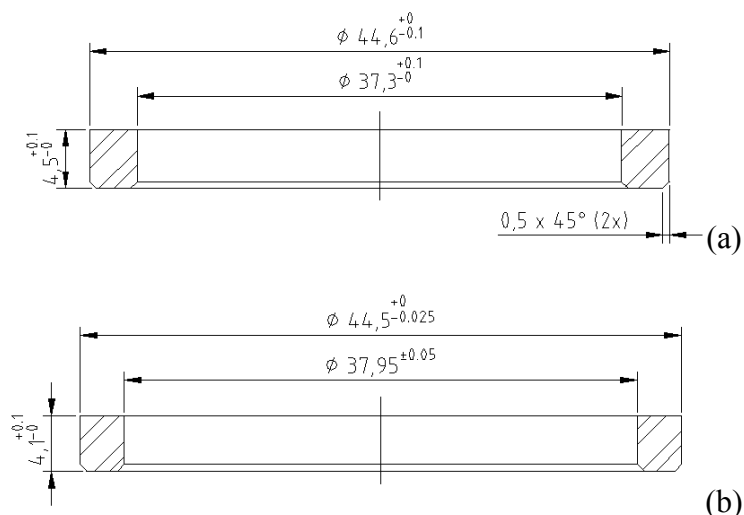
Desenho do corpo-de-prova destinado para aplicação de pré-tensão com as dimensões pós-torneamento (a) e pós-retificação (b).
